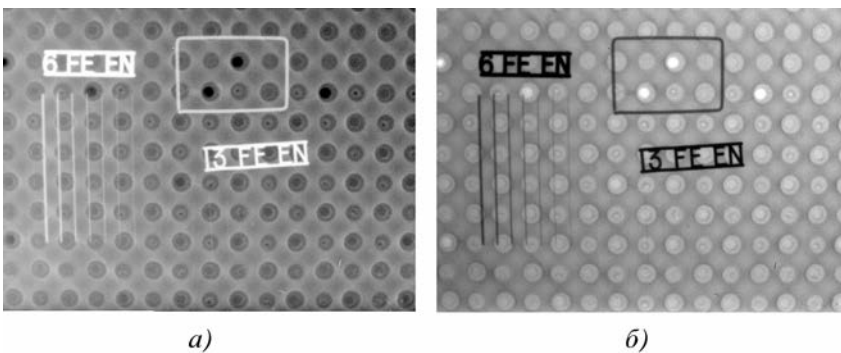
Цифровые изображения образца с двойной точечной сваркой с локализацией участка для исследования с помощью твердотельного преобразователя:
